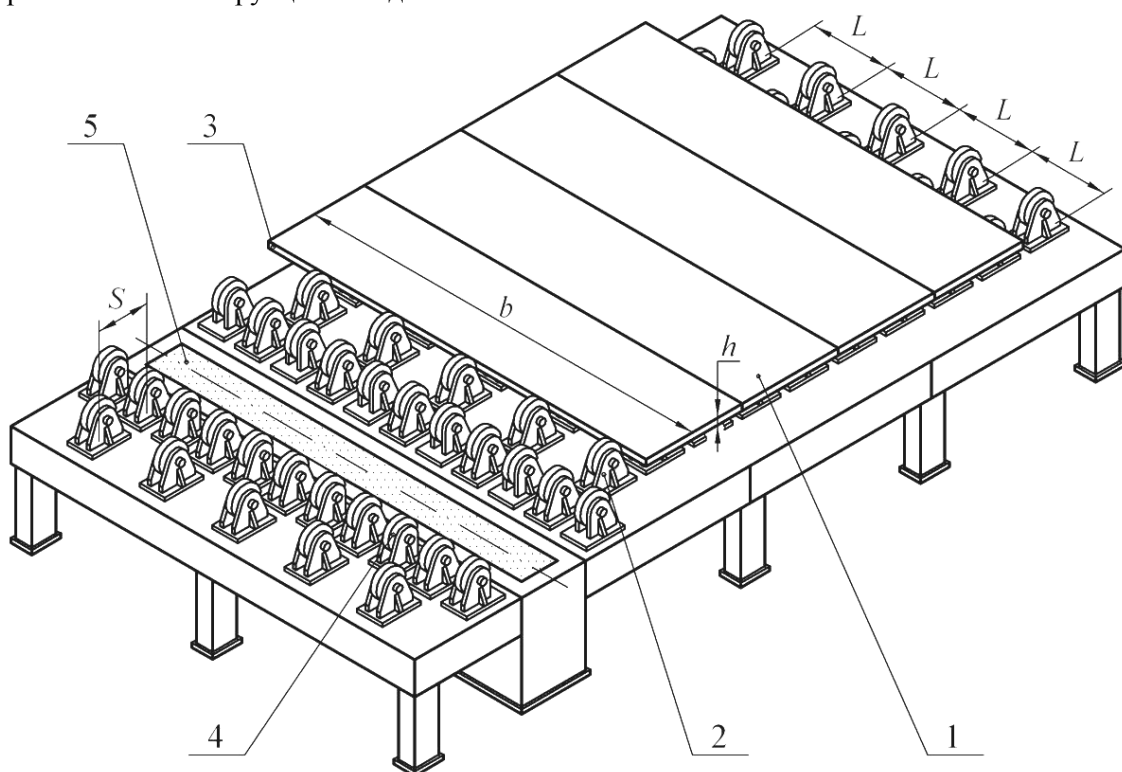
Фрагмент роликового поля линии сборки и сварки тонколистовых полотнищ:
